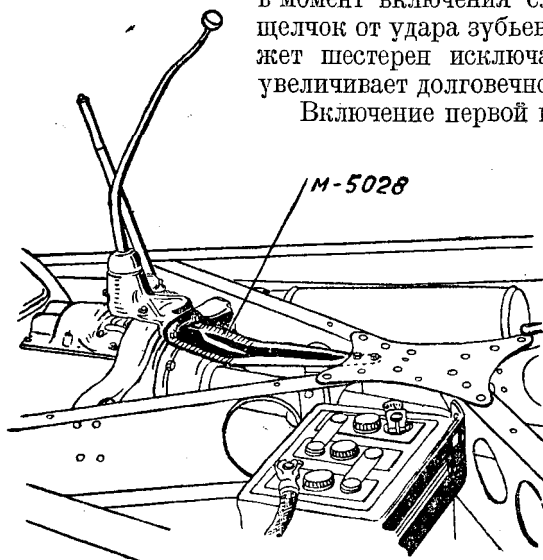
Усилитель поперечины рамы в месте крепления колонки механизма переключения передач.
